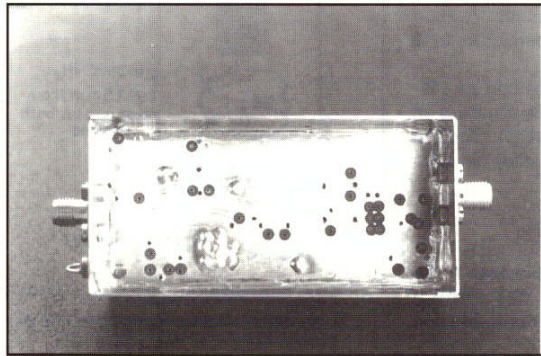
Preparazione per il montaggio: dopo la foratura il PCB è stato posizionato con la superficie tutto rame a 16 mm dal bordo superiore della scatola e con il lato piste (componenti SMD) a 11 mm dal bordo inferiore. Il PCB deve essere saldato alla scatola per tutta la lunghezza delle pareti.
